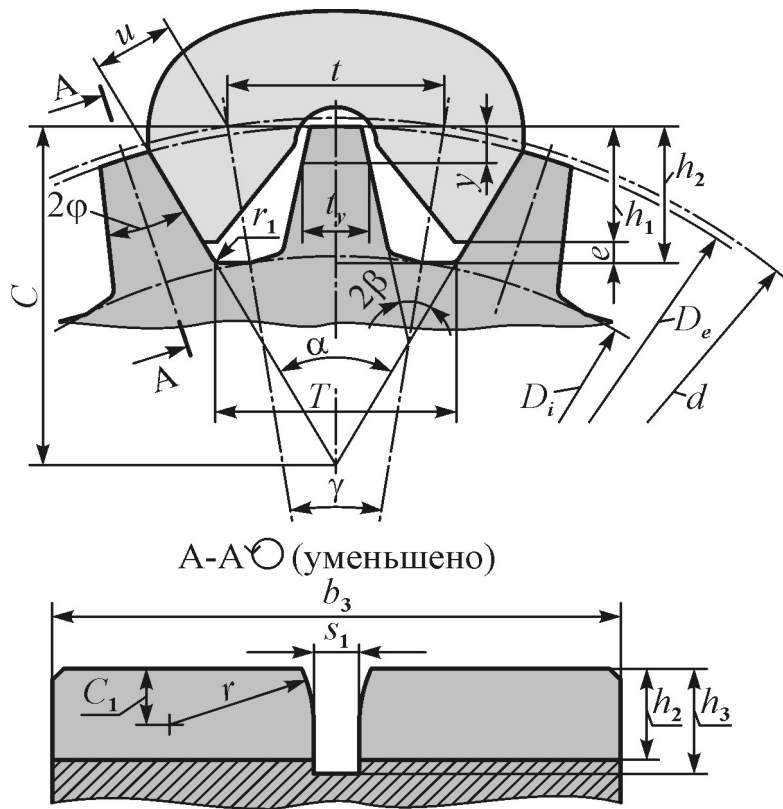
Профиль зубьев звездочки для зубчатой цепи типа ПЗ-1
